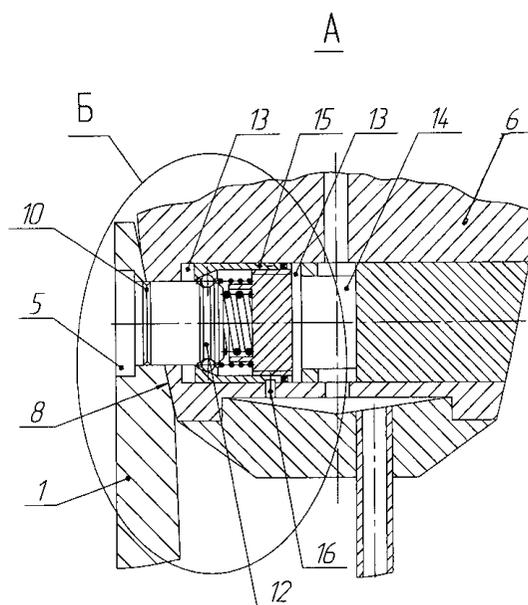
Соединительный узел режущего инструмента с клином и отсоединительным устройством в транспортном положении
